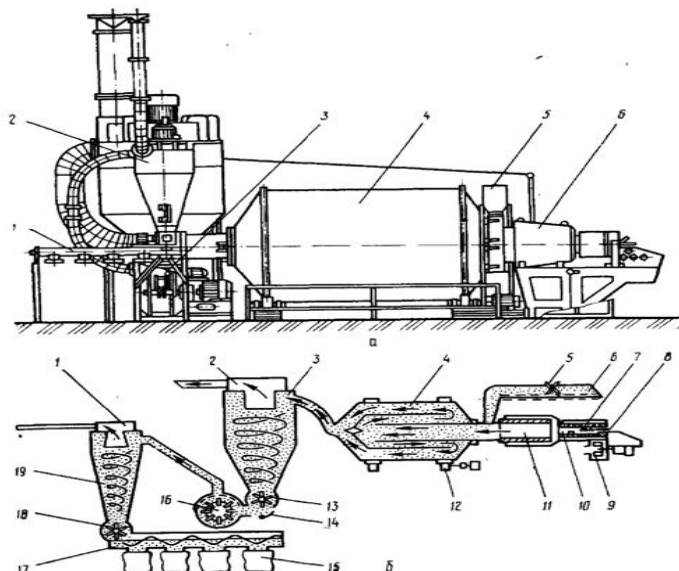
Барабанний сушильний агрегат АВМ-04
